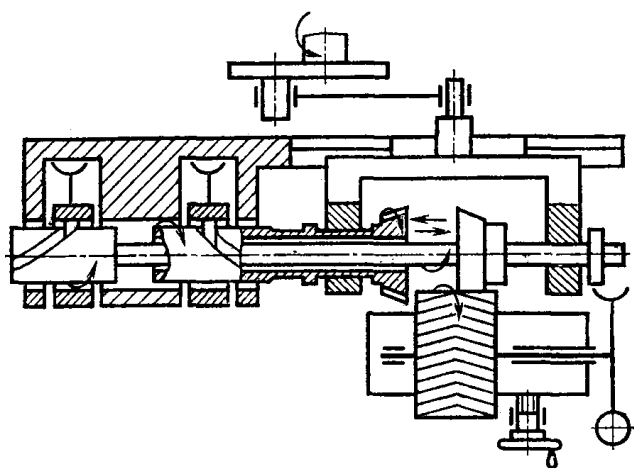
Схема довбання зубів шевронного колеса
